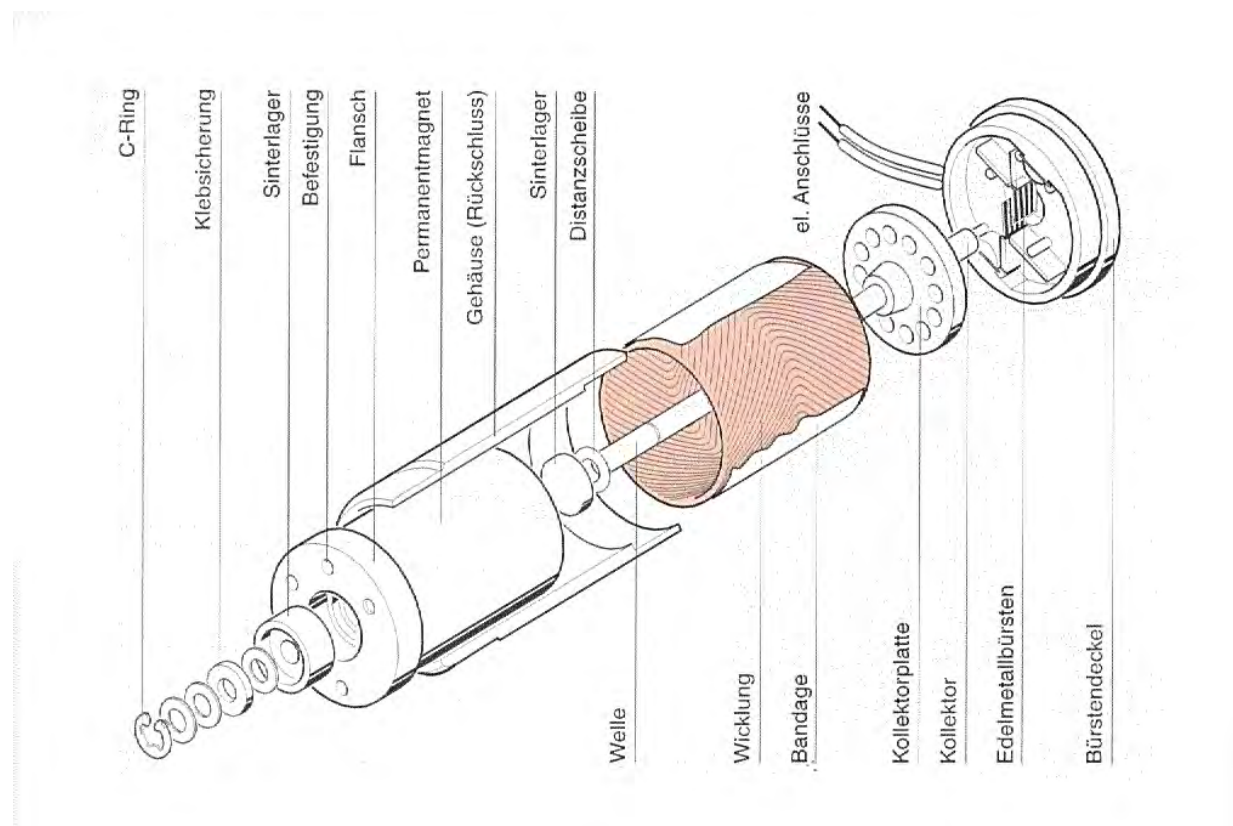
Glockenankermotor mit stirnseitigen Bürsten
